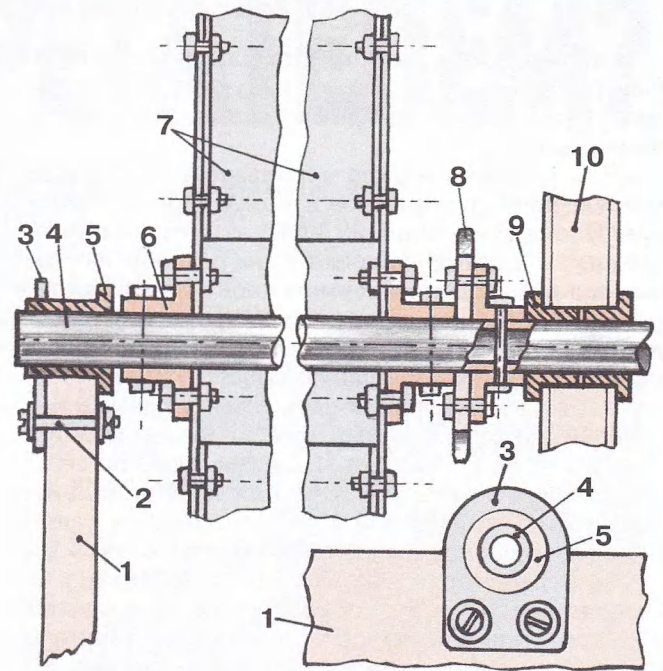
Конструкция ведущего вала: 1 — продольная доска каркаса поплавка; 2 — винт; 3 — втулка-скоба; 4 — ось вала; 5 — пластиковая втулка; 6 — фланец; 7 — лопастное колесо; 8 — ведомая звездочка цепи; 9 — пластиковая втулка; 10 — центральная часть корпуса.
